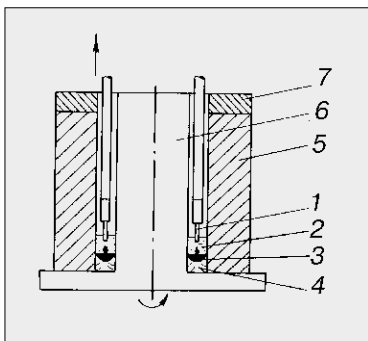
Схема ЭШН внутренней цилиндрической поверхности: 1 — электрод; 2 — шлаковая ванна; 3 — металлическая ванна; 4 — наплавленный слой; 5 — заготовка; 6 — медный охлаждаемый стержень; 7 — выводная втулка
